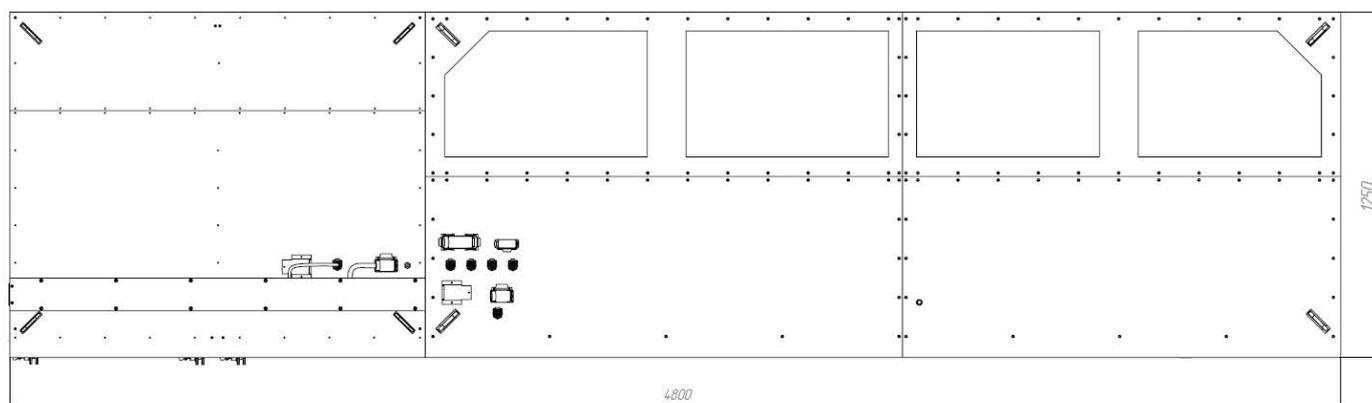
АТ27-М40...М63-6/6-XXXXXX-С-43. Вид сверху
